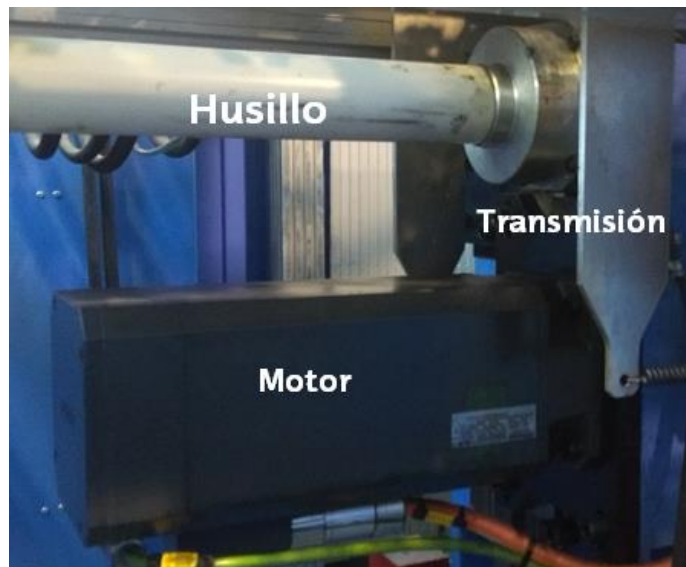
Motor y transmisión polea-correa hasta eje de husillo
